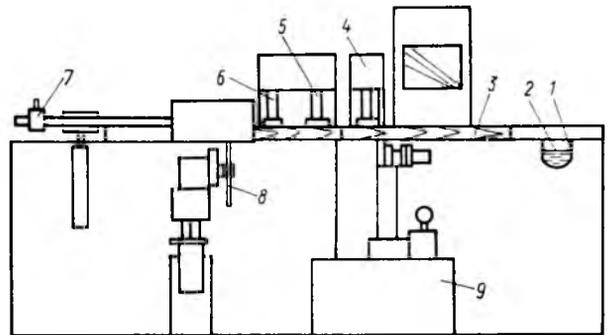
Пресс для склеивания брусовых деталей на зубчатый шип:
